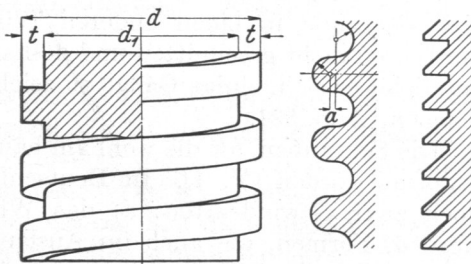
326. Flach-, Rund- und Sägegewinde.
